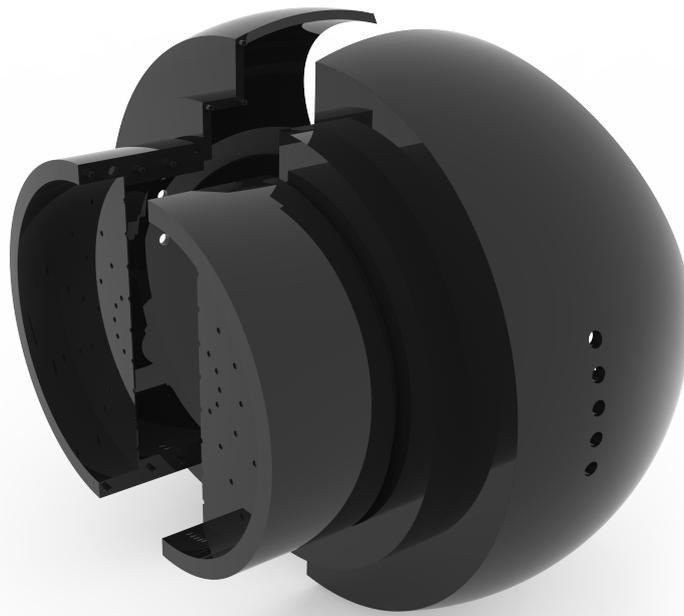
Render 2 de ACCOM One sin almohadilla y explosionado
